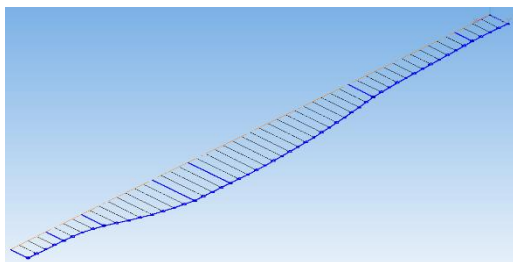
Ескіз розрахованого контуру робочої поверхні резонаторної труби
